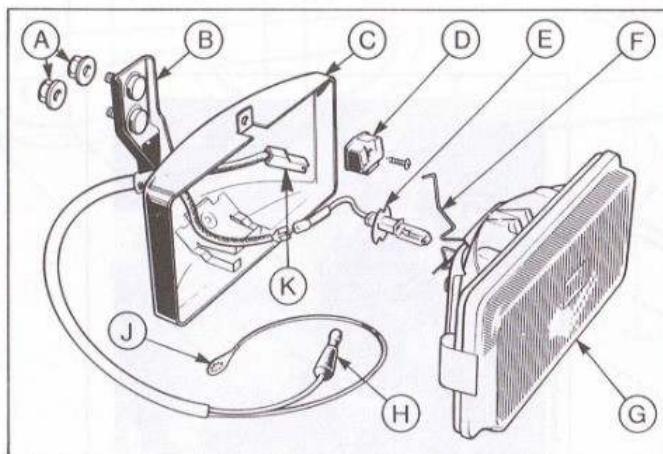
Disposición de los componentes de un faro auxiliar.
